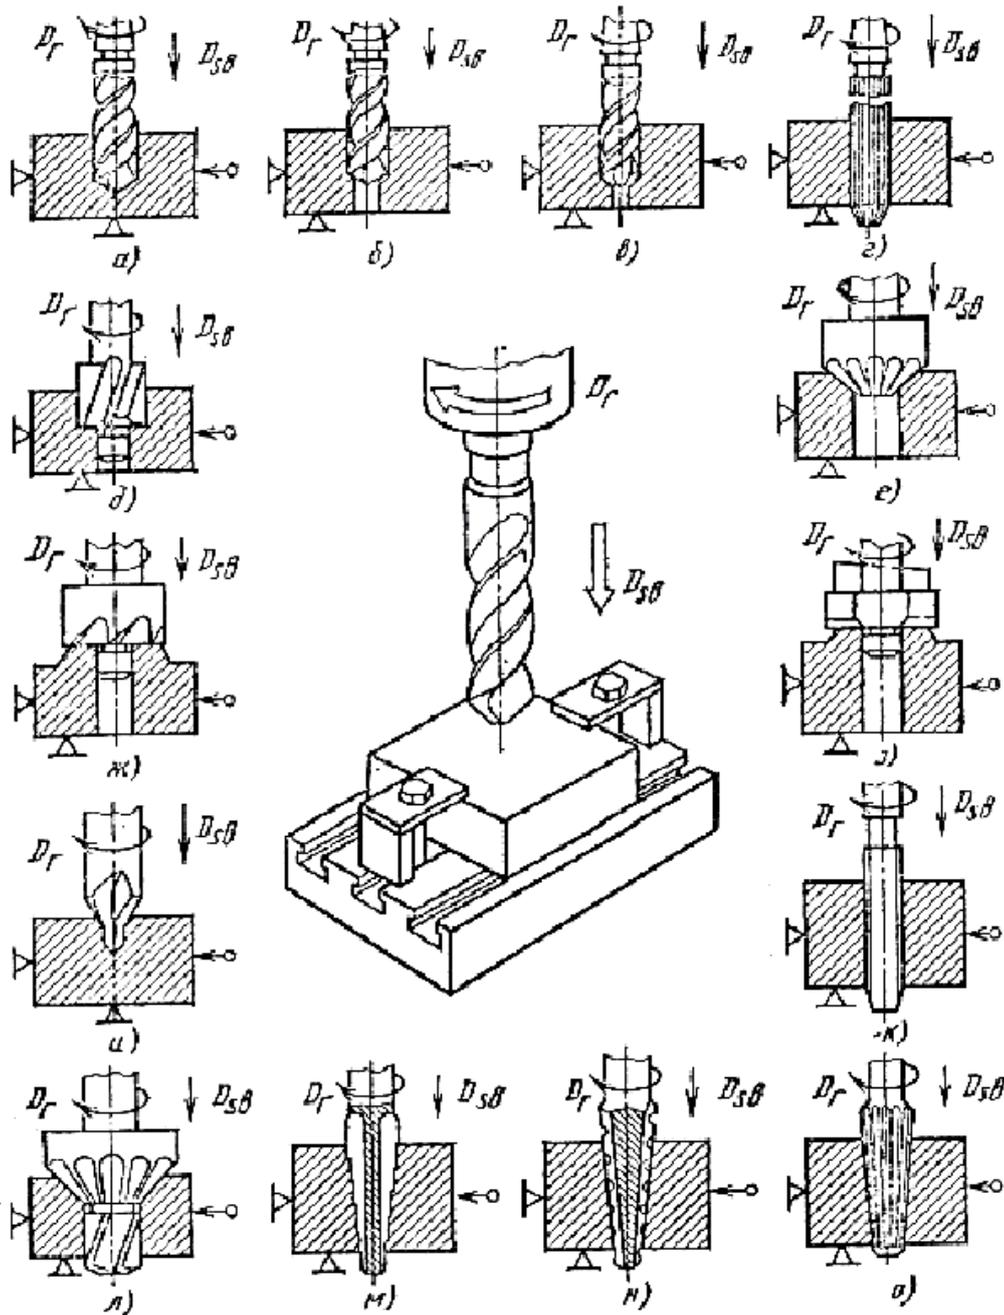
Схемы обработки заготовок на сверлильных станках
